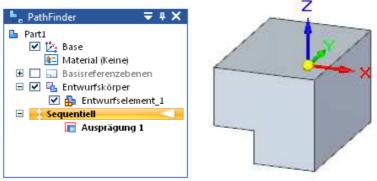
Die Ausprägung im PathFinder und in der Ansicht
